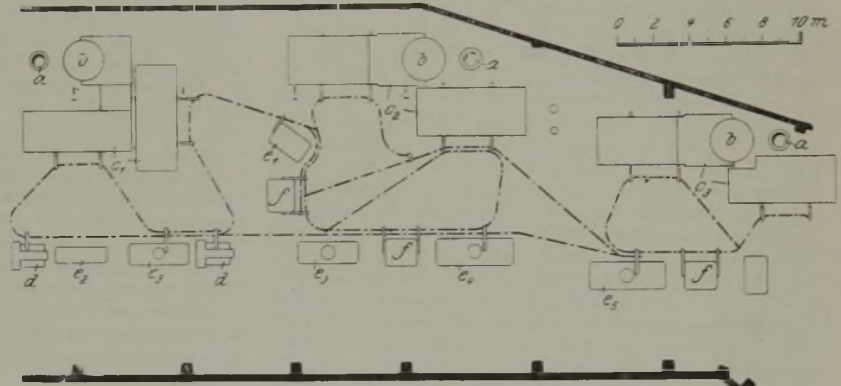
Schmiede der Champion Machine & Forging Co.
